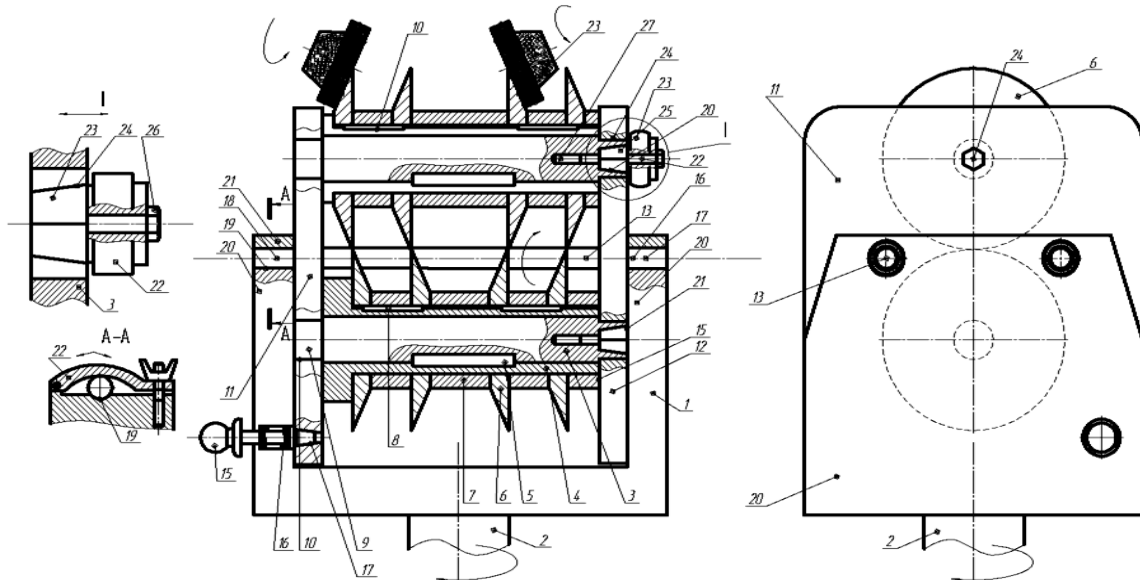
Верстат для заточування ножових блоків для розрізання гладкої конвеєрної стрічки на смуги
